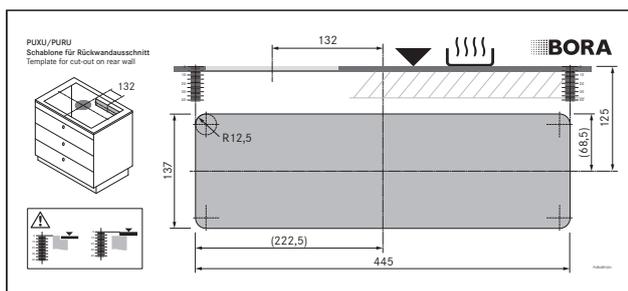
Montážní rozměry při recirkulaci, hloubka pracovní desky od 675 mm
